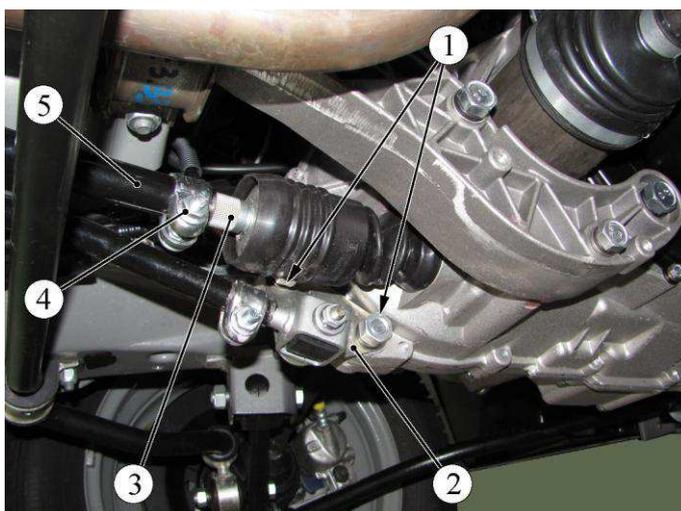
Отсоединение реактивной тяги и тяги привода коробки передач:
